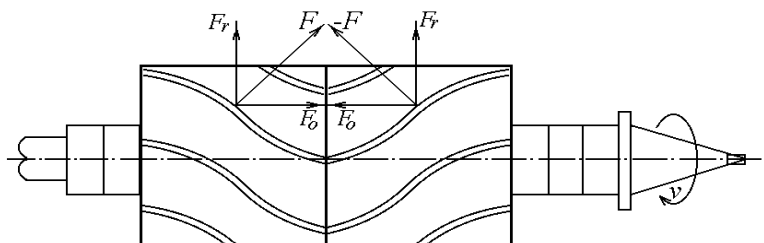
Схема розподілу сил при фрезеруванні складеними фрезами
